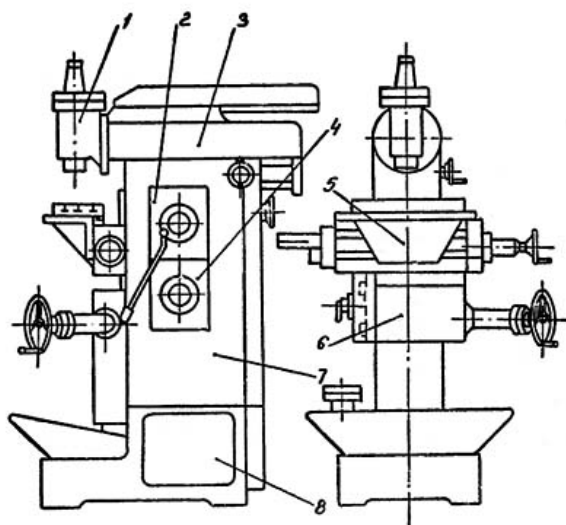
Общий вид широкоуниверсального фрезерного станка 676П.
